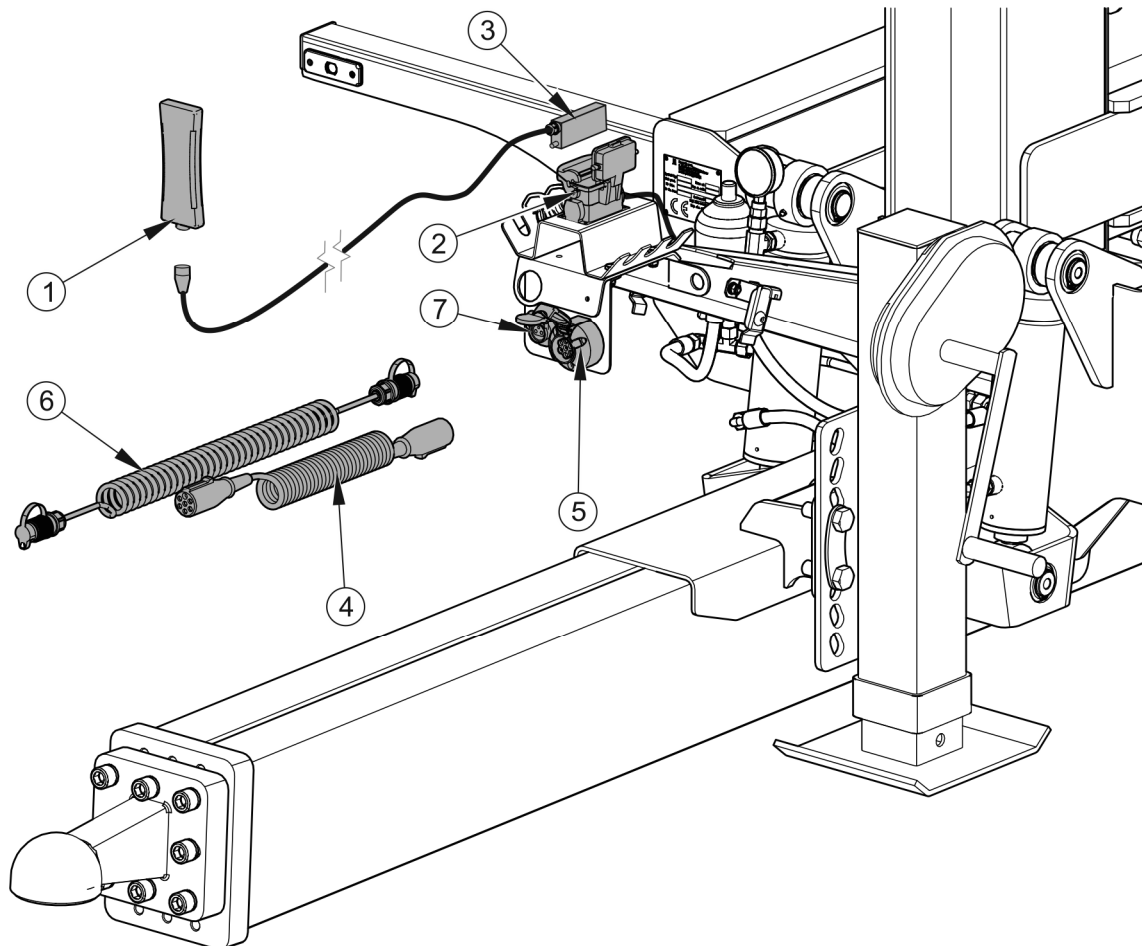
Kobling til hydraulisk støtteinstallasjon
